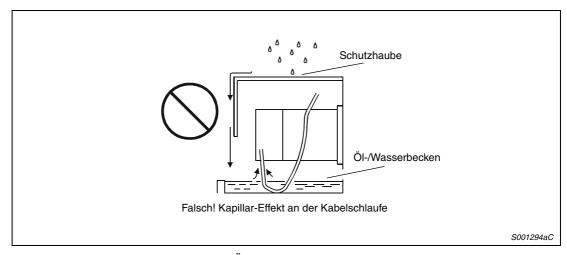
Kabel zum Motor nicht in Öl oder Wasser liegend verlegen
